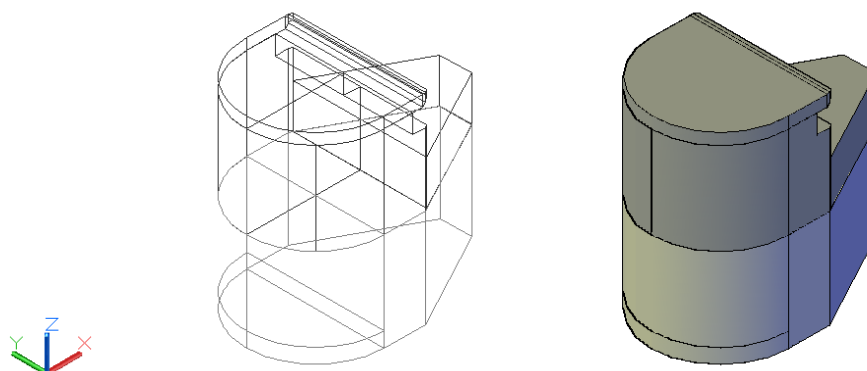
Ocelový plášť PITu s betonovým základem
